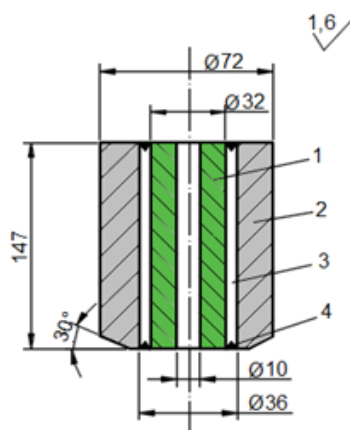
Конструкция биметаллической заготовки: 1 – внутренняя трубная заготовка (ВТбс); 2 – внешняя трубная заготовки (1201); 3 – вакуумирований зазор; 4 – герметизирующие и токоизолирующие кольцевые клинья
